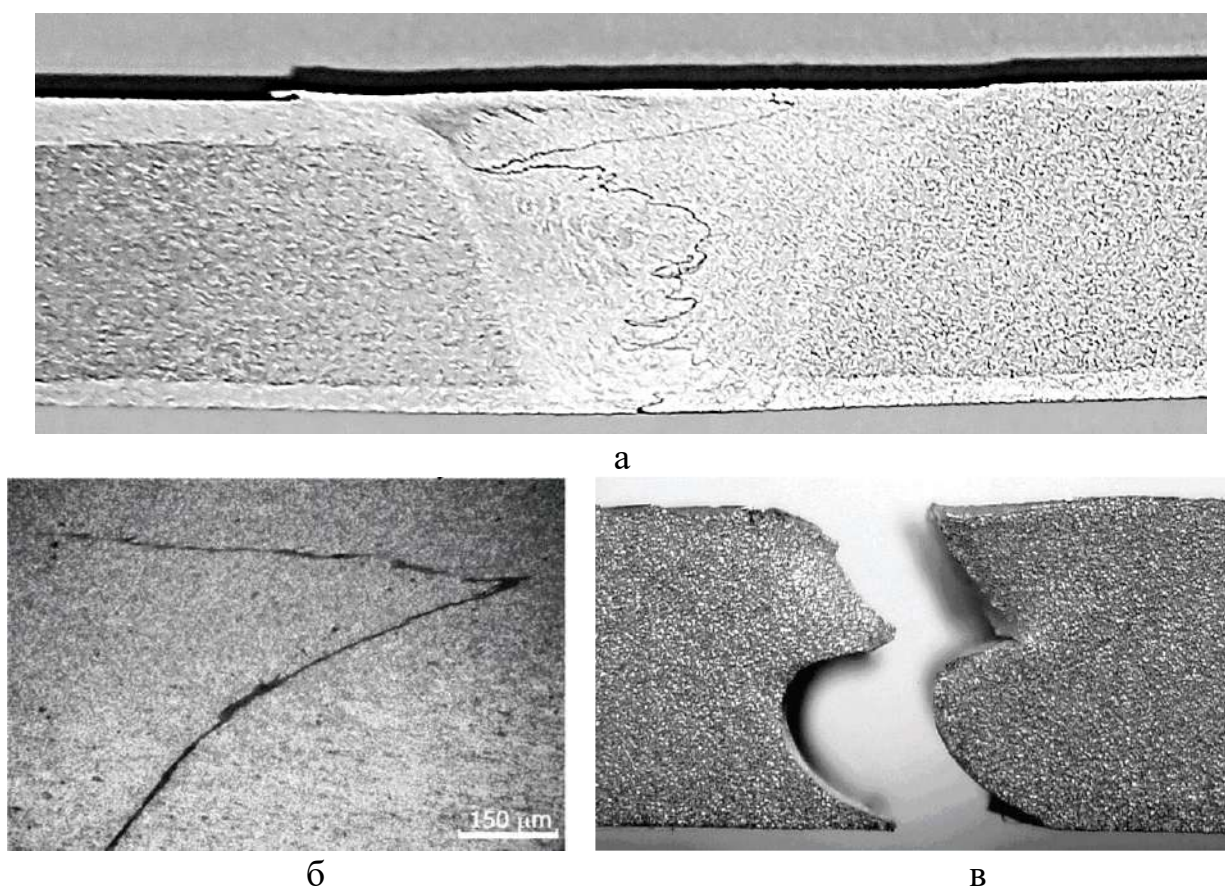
Линия стыка на поперечном сечении сварного шва сплава 6082Т6 (а) и фрагмент разрушенного образца (б); в – разрушение материала по полосам луковичной структуры
